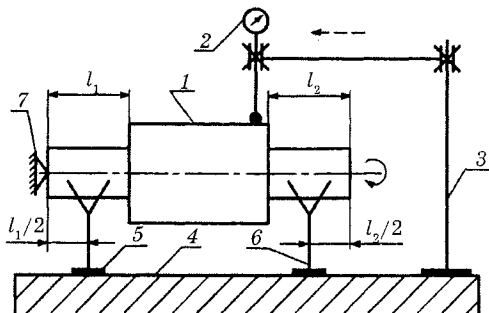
Измерение радиального биения наружной номинально цилиндрической поверхности относительно общей оси двух наружных базовых поверхностей:
